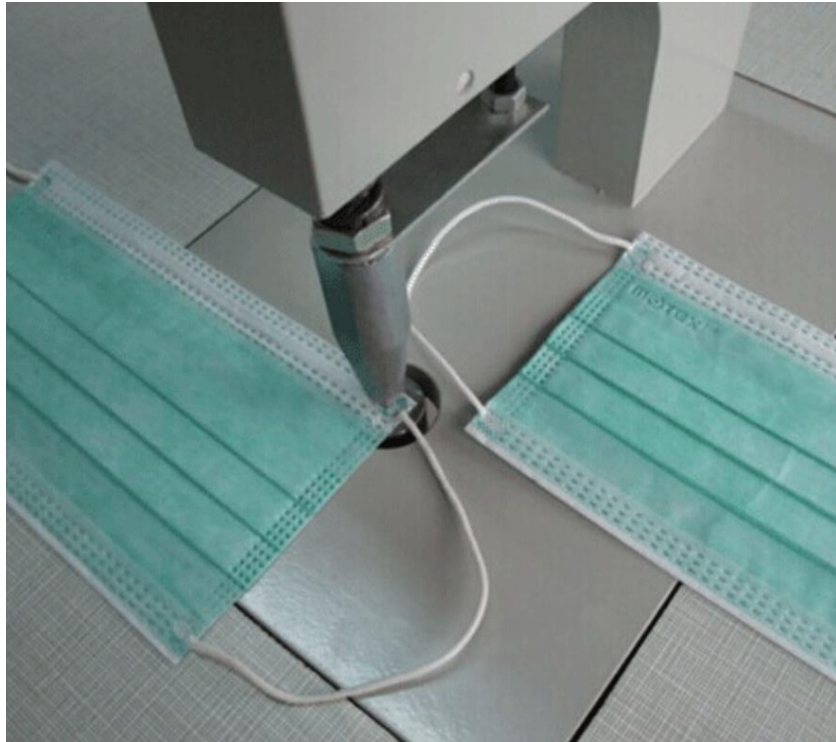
Зовнішній вигляд маніпулятора зварювання
